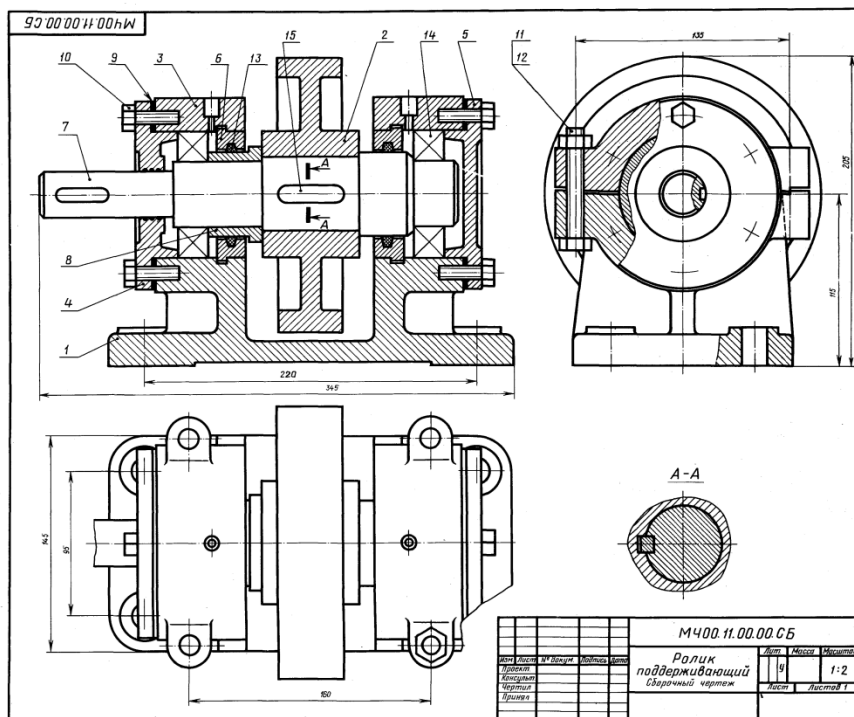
Сборочный чертеж «Ролик поддерживающий»
